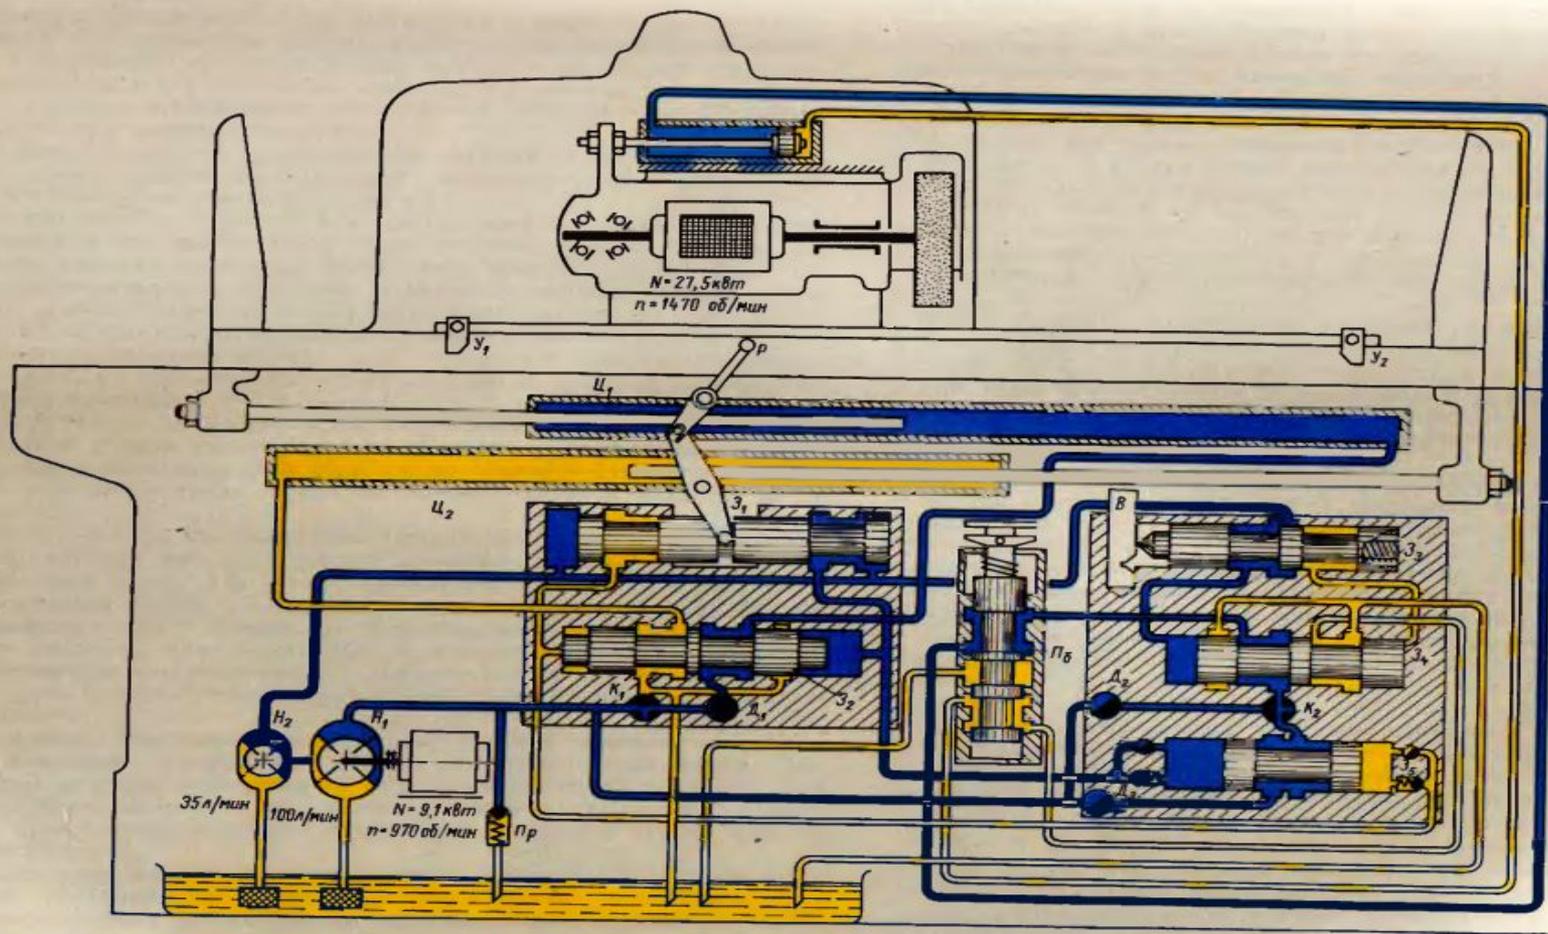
Гидравлическая схема плоскошлифовального станка модели 3724
